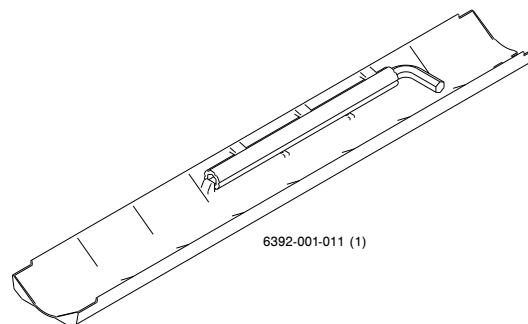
Sechskantschlüssel und Ausbauwerkzeug-Verlängerung
